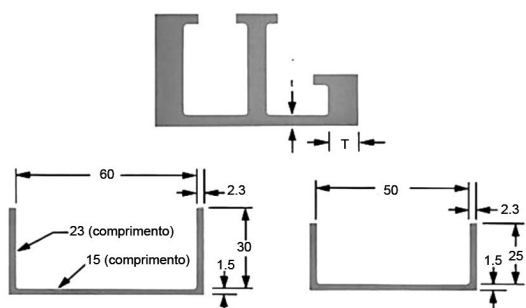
Dimensões (mm) recomendadas para perfis de parede não uniformes em PPE/PS
